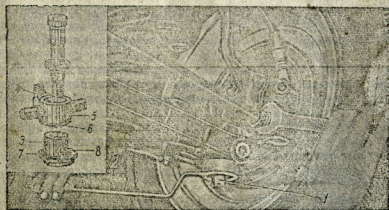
Регулировка углов развала и схождения передних колес: 1 — гайка пальца стойки; 2 — специальный ключ; 3 — эксцентриковая втулка; 4 — ушко опоры стойки для ограничительного болта; 5 — опоры стойки; 6 — зубчики опоры стойки; 7 — зубчики эксцентриковой втулки; 8 — треугольная выемка-метка
